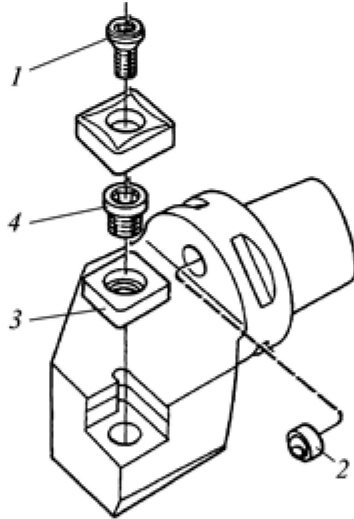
Унифицированная конструкция проходного резца SCLC с пластиной ССМТ, закрепленной винтом: 1 — винт; 2 — втулка для подвода СОЖ; 3 — подкладка; 4 — резьбовая втулка
